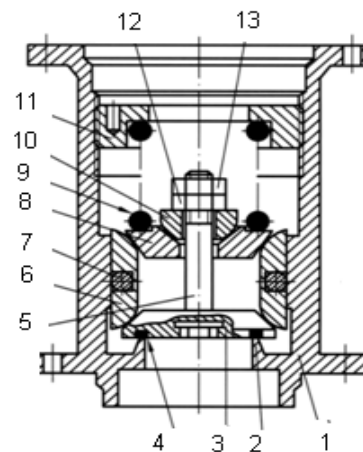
Пружинный клапан с соединением звеньев «направляющая-клапан-седло» закладными шарнирами пространственного положения 1 - корпус; 2 - седло; 3 - клапан; 4 - клапанное уплотнение; 5 - резьбовой хвостовик клапана; 6 - набор разрезных полушайб; 7 - браслетная пружина; 8 - закладной конус; 9 - пружина; 10 - закладная сфера; 11 - резьбовой пружинный подпятник; 12 - гайка; 13-контргайка
